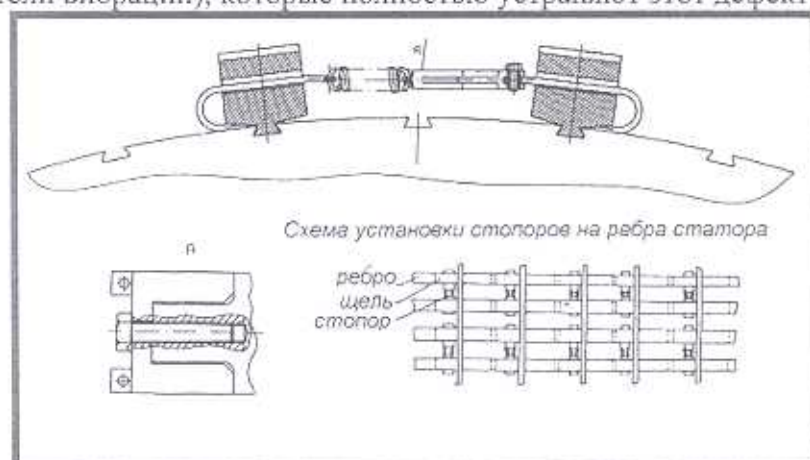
Приспособление для стяжки ребер сердечника статора генераторов ТВВ
